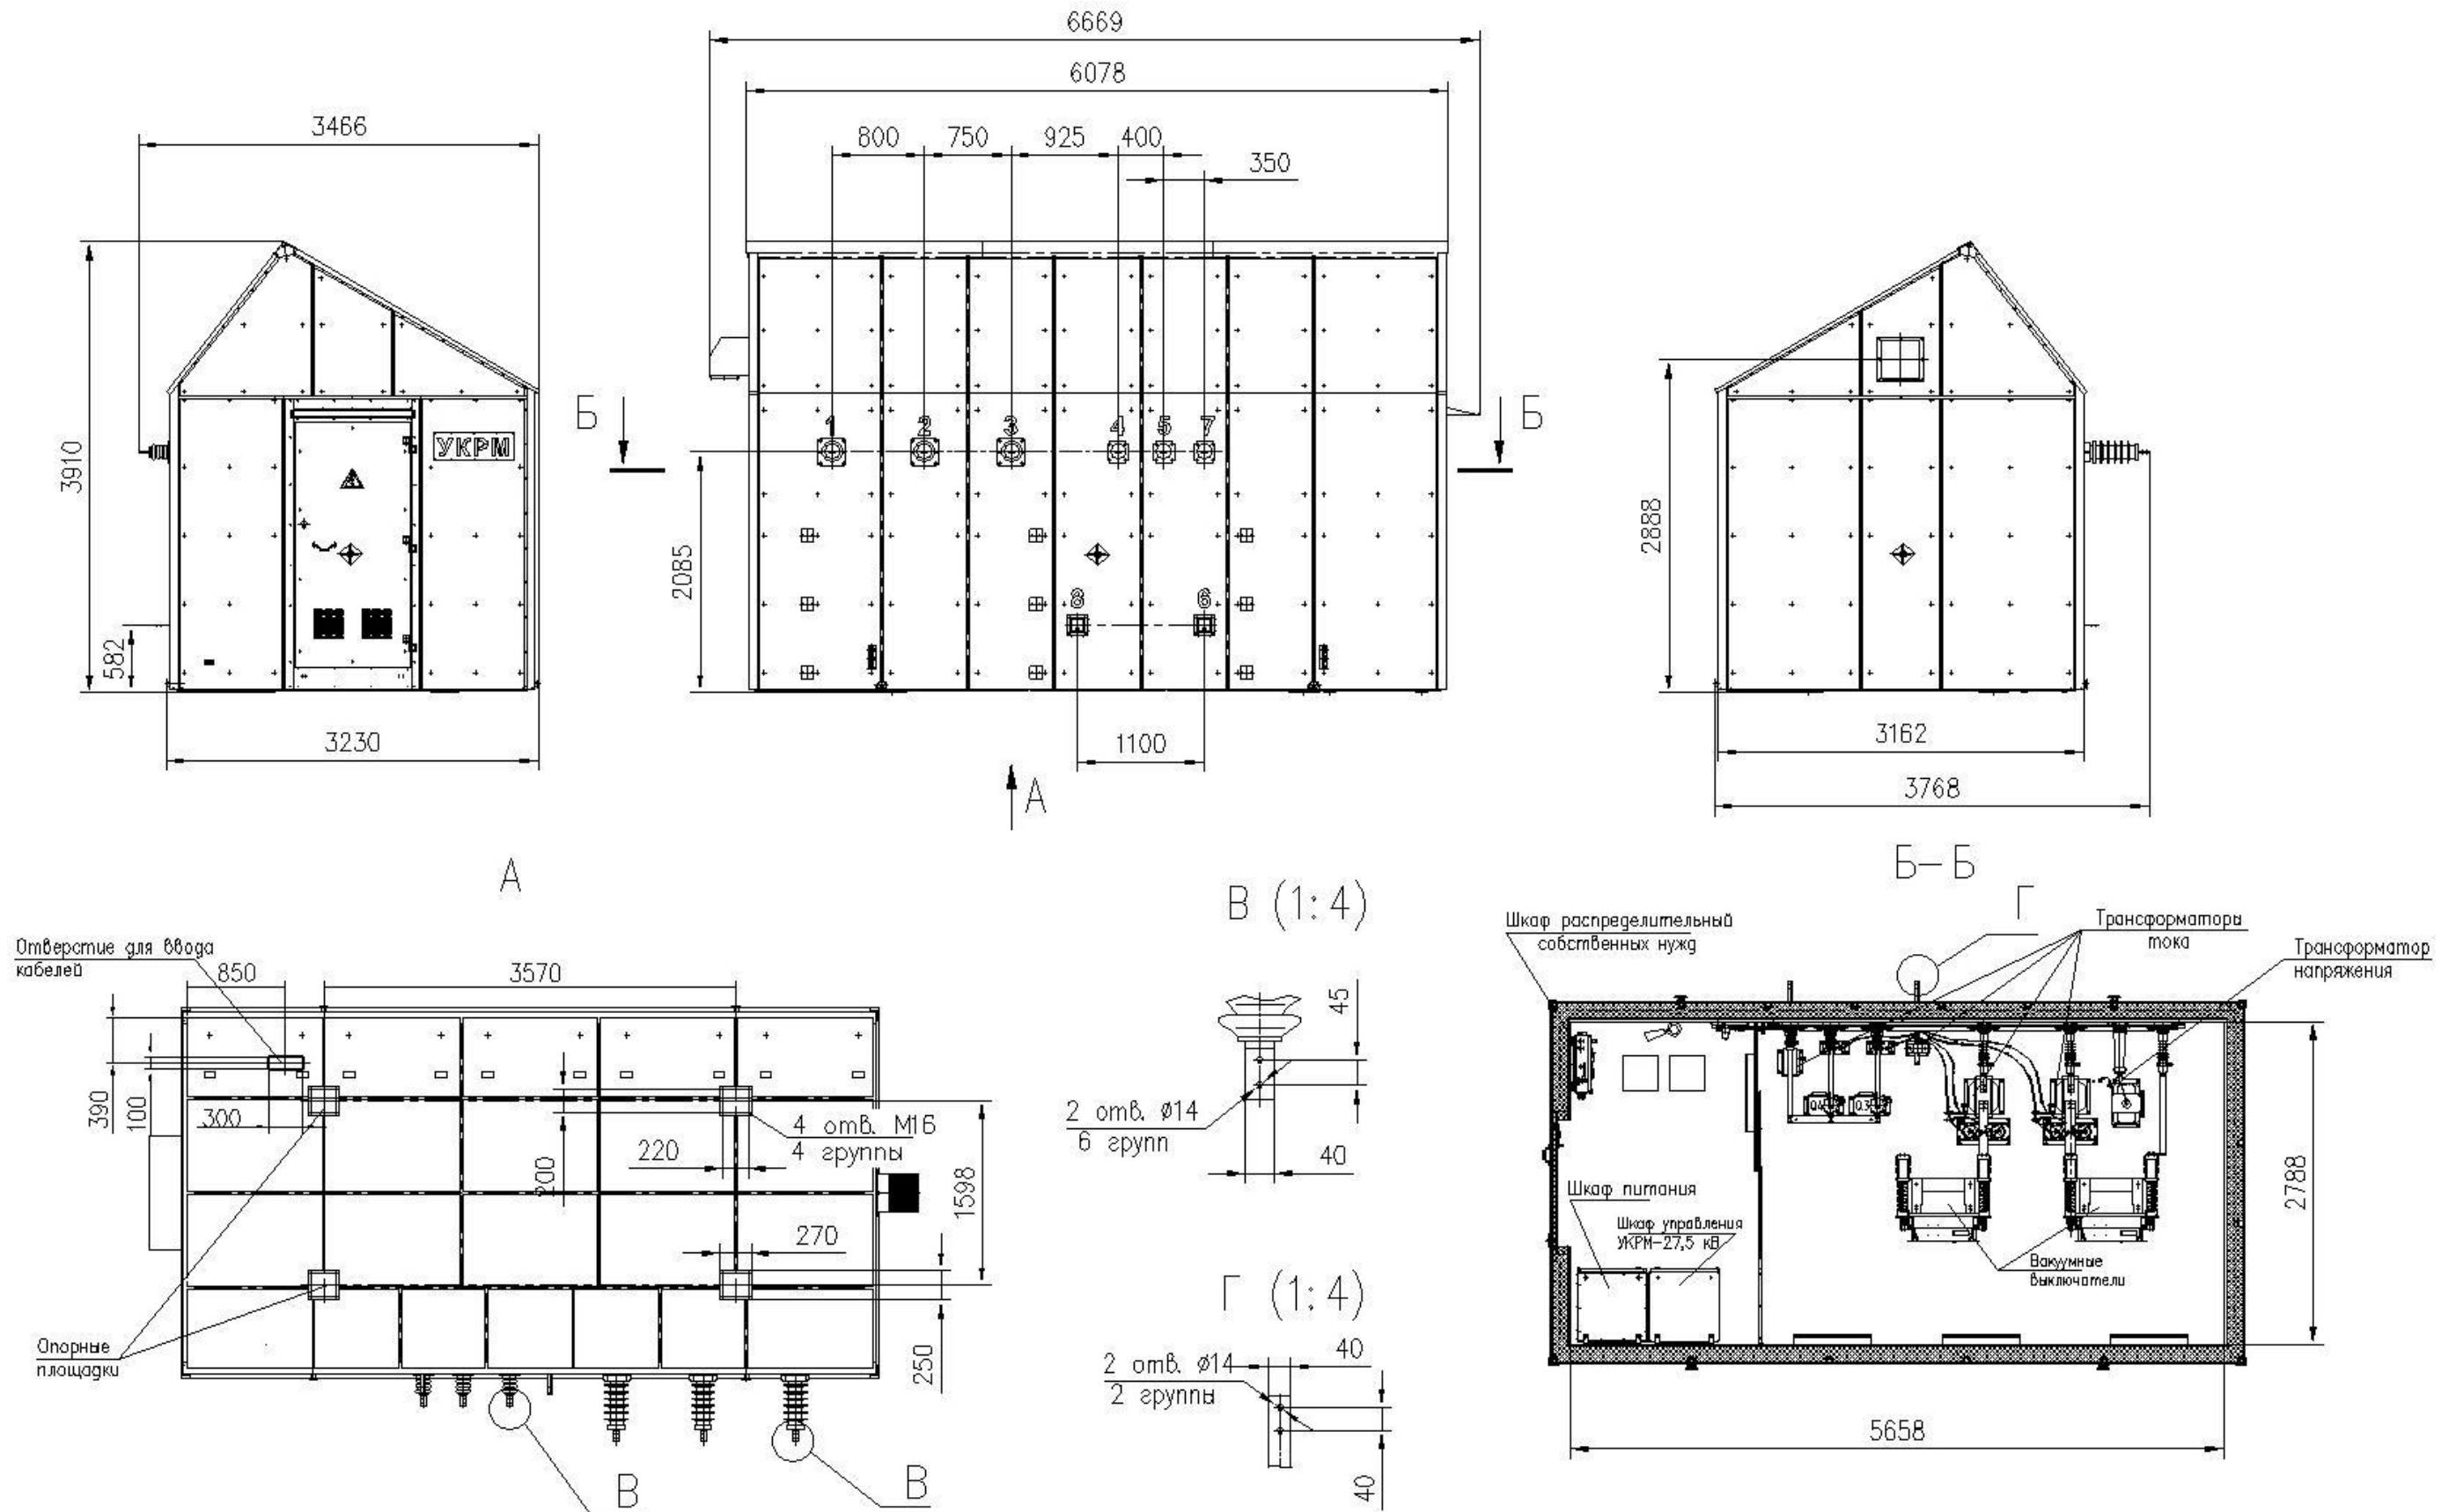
Габаритный чертеж модуля управления УКРМ-27,5 кВ типоразмером 6 м
